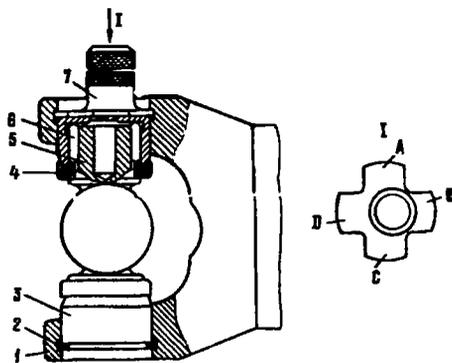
Сборка карданного шарнира: 1 - вилка карданного шарнира; 2 - стопорное кольцо; 3 - корпус подшипника; 4 - сальник; 5 - шип крестовины; 6 - игла подшипника; 7 - мерный щуп; А, В, С, D - лепестки щупа, имеющие толщину 1,53; 1,56; 1,59; 1,62 мм
